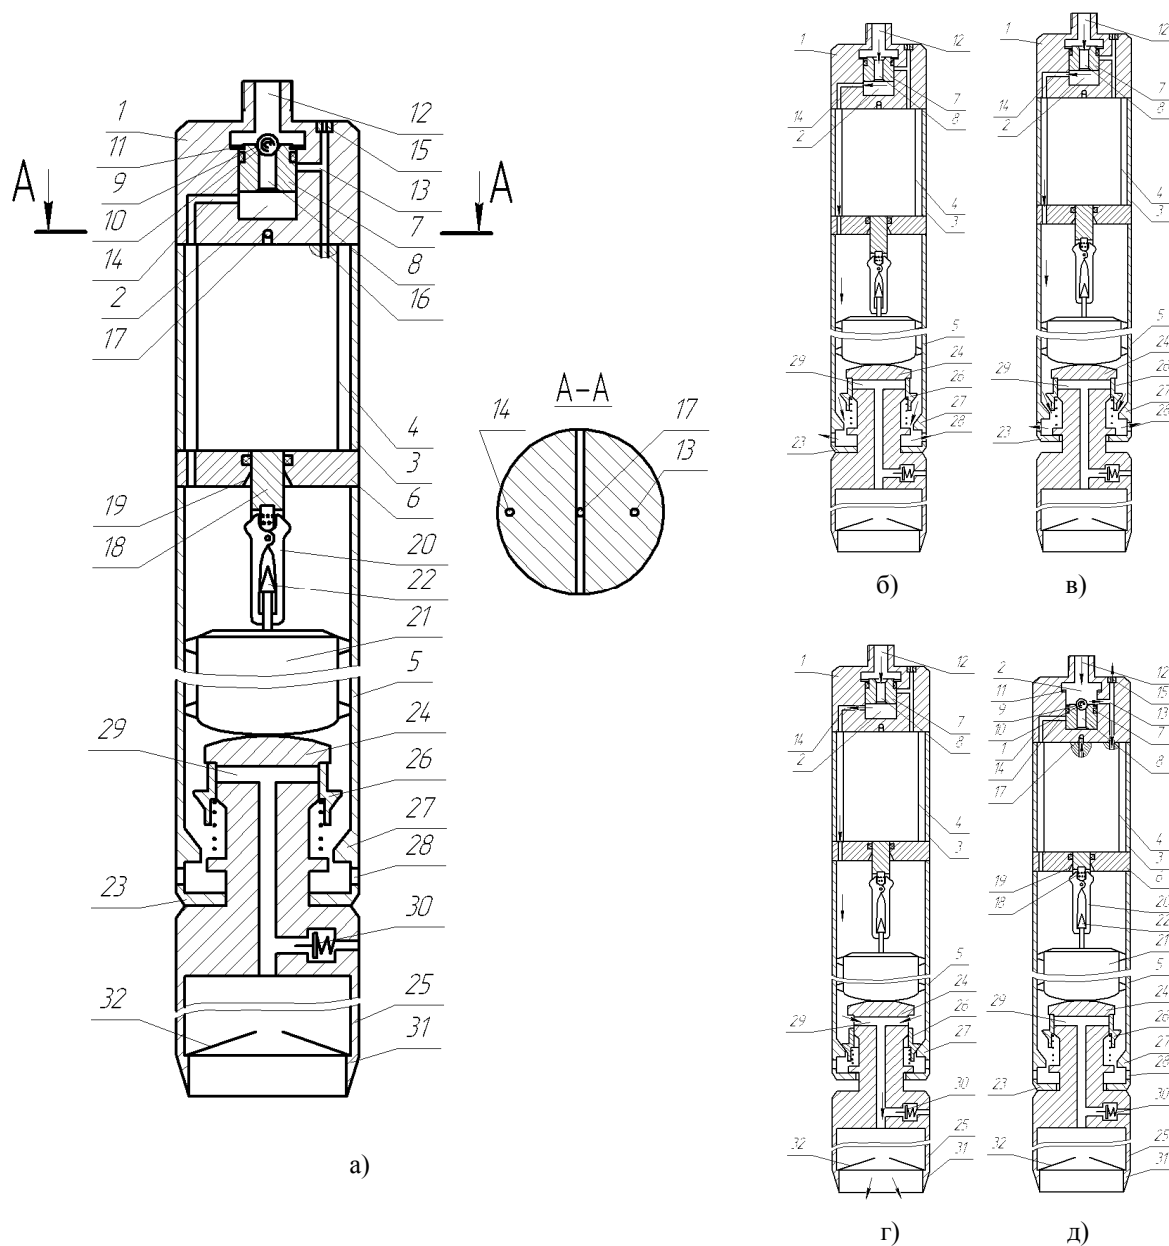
Конструкция и принцип действия забивного пробоотборника: 1 – распределительный переходник; 2 – камера; 3 – кожух; 4 – корпус гидродвигателя; 5 – корпус ударного узла; 6 – перегородка; 7 – поршень; 8 – канал; 9 – седло; 10 – пусковой клапан; 11 – штифты; 12, 13, 14 – каналы; 15 – дроссельная втулка; 16 – входная полость гидродвигателя; 17 – выхлопной канал гидродвигателя; 18 – шток гидродвигателя; 19 – коническая поверхность; 20 – захваты; 21 – боек; 22 – коническая головка; 23 – нижний переходник; 24 – наковальня; 25 – колонковая (керноприемная) труба; 26 – кольцевой клапан-золотник; 27 – седло; 28 – отверстия; 29 – канал в наковальне; 30 – обратный клапан; 31 – башмак; 32 – кернорватель.
